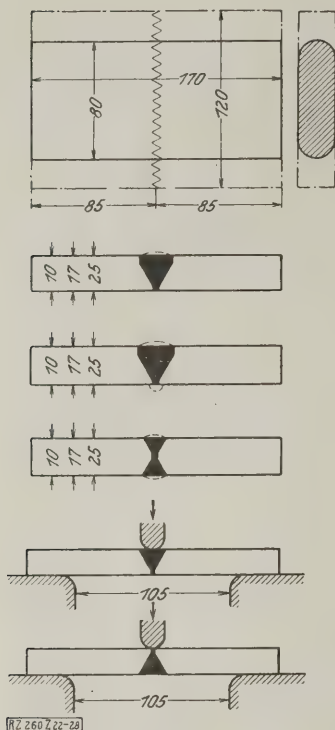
bis 28. Elektrisch geschweißte Biegeprobestäbe; verschiedene Belastungsart.
